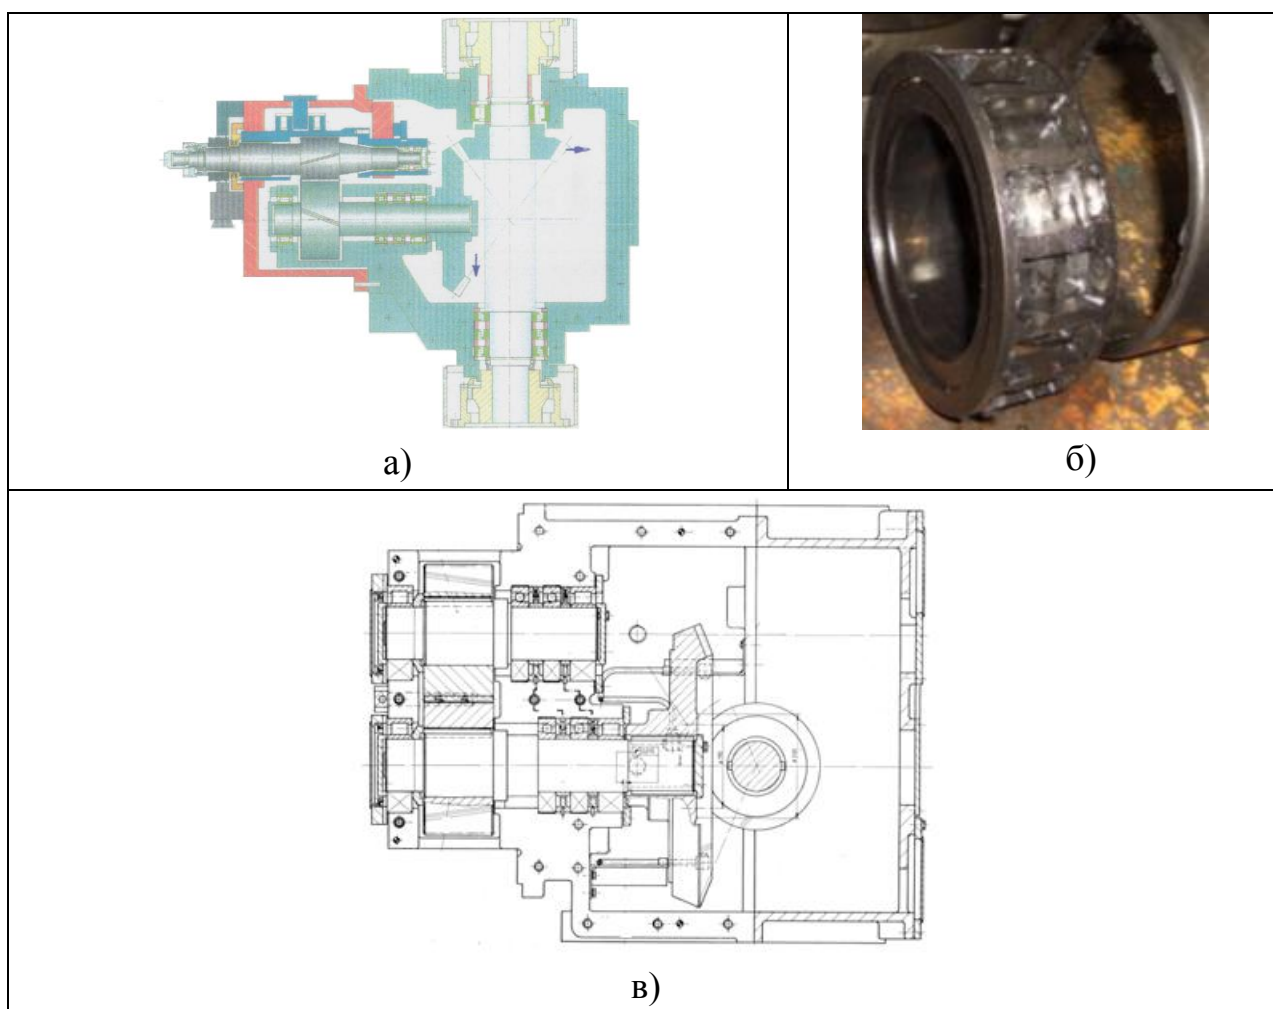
Схема расположения редукторной и валковой кассет (а), характерный вид повреждений роликоподшипника (б), схема редукторной кассеты (в)
